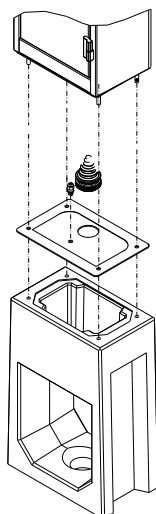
Vista esplosa della stazione di ricarica da montare su base
